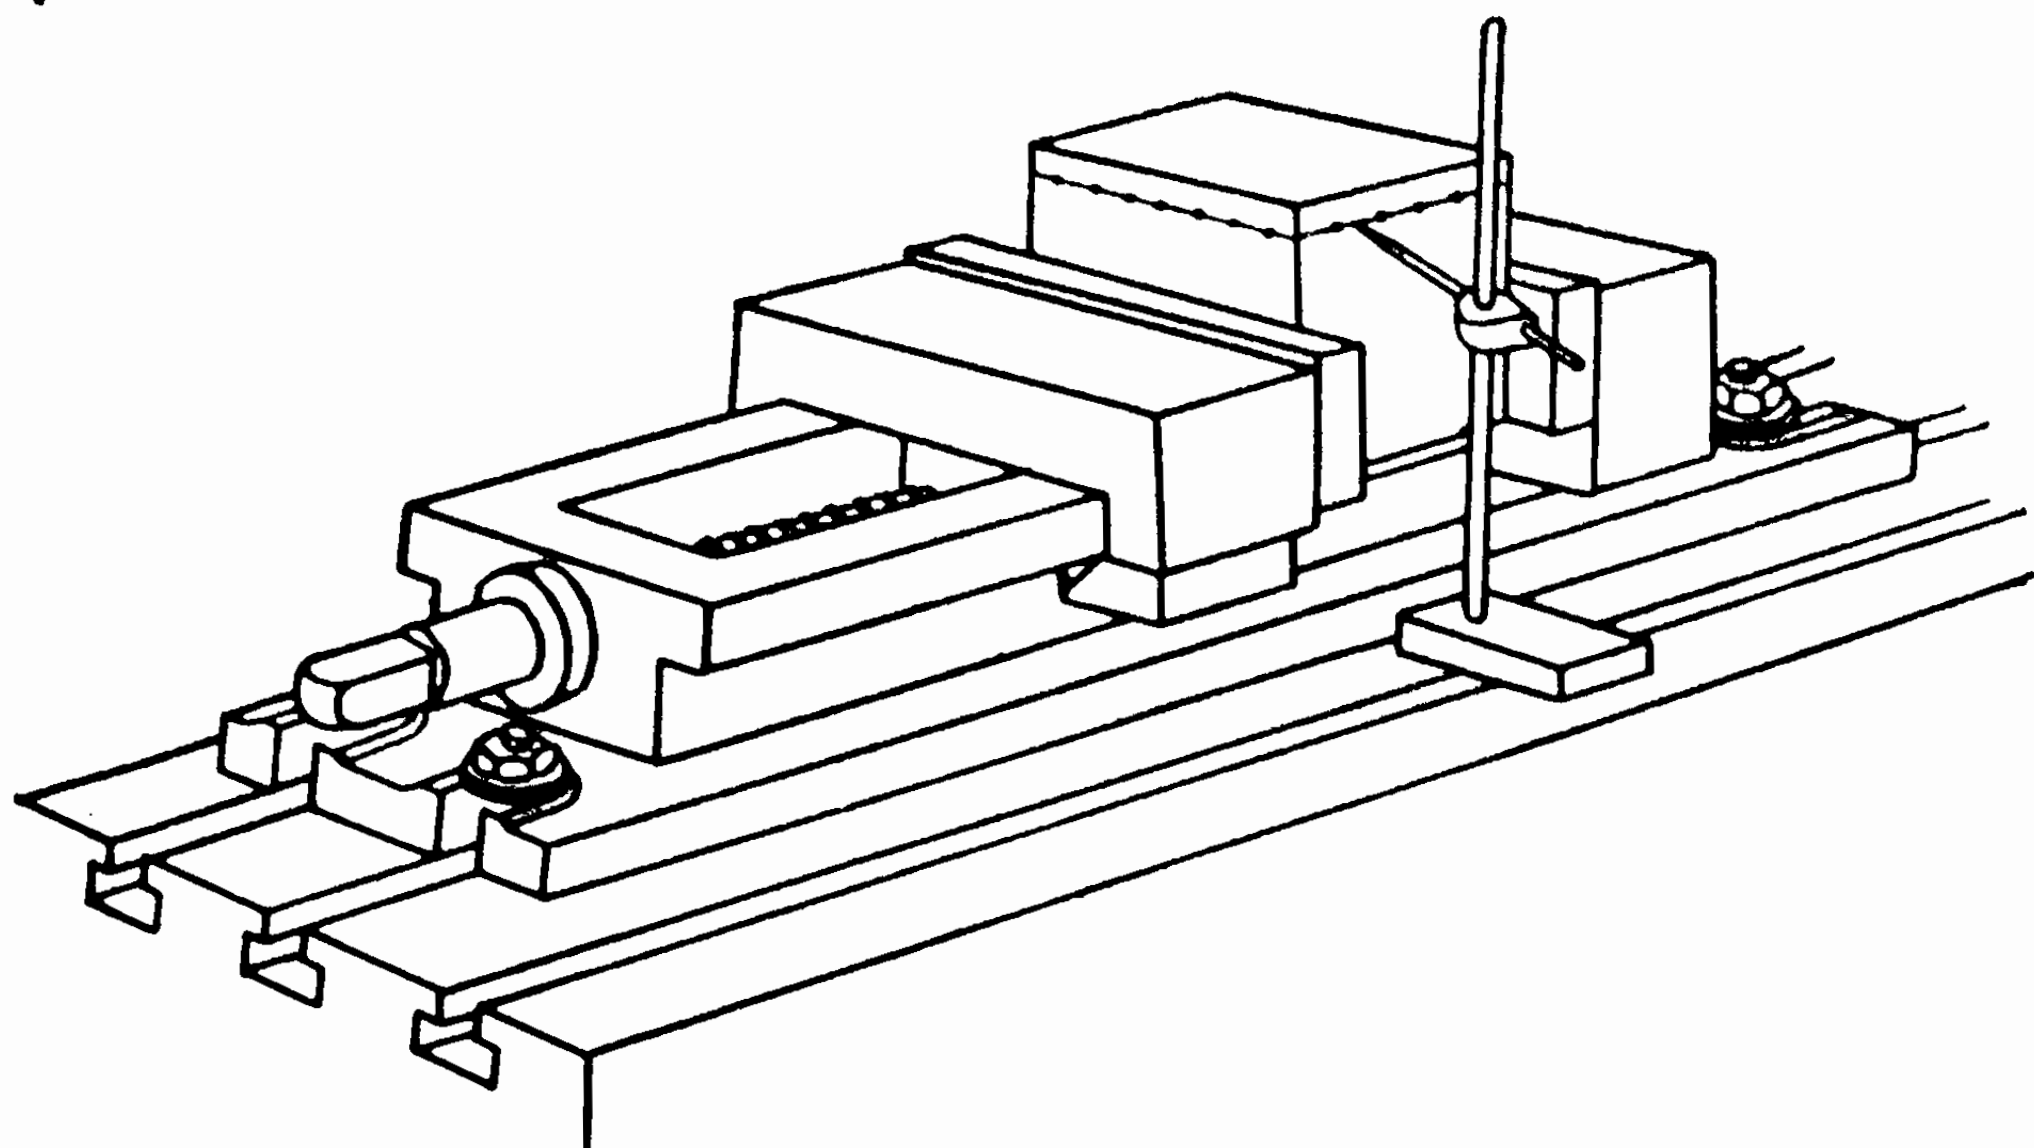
Выверка заготовки по линиям разметки рейсмасом.
